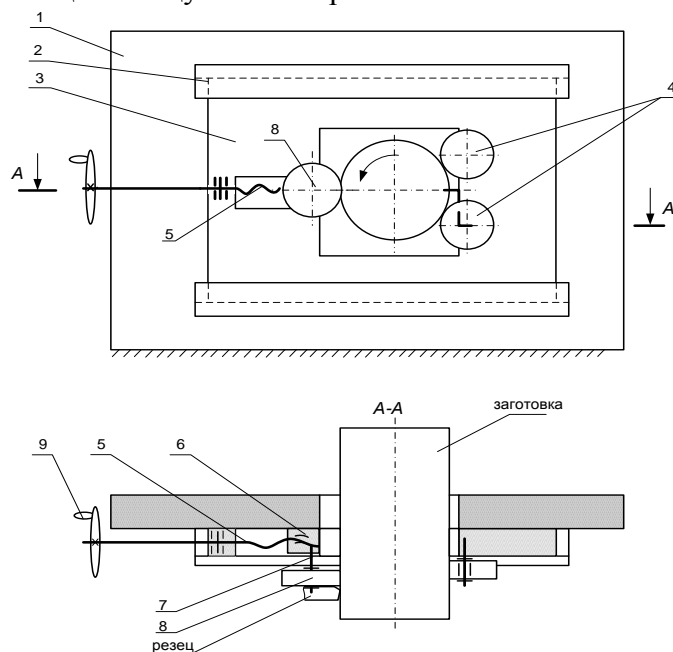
Схема устройства для обработки заготовок из пластмасс
